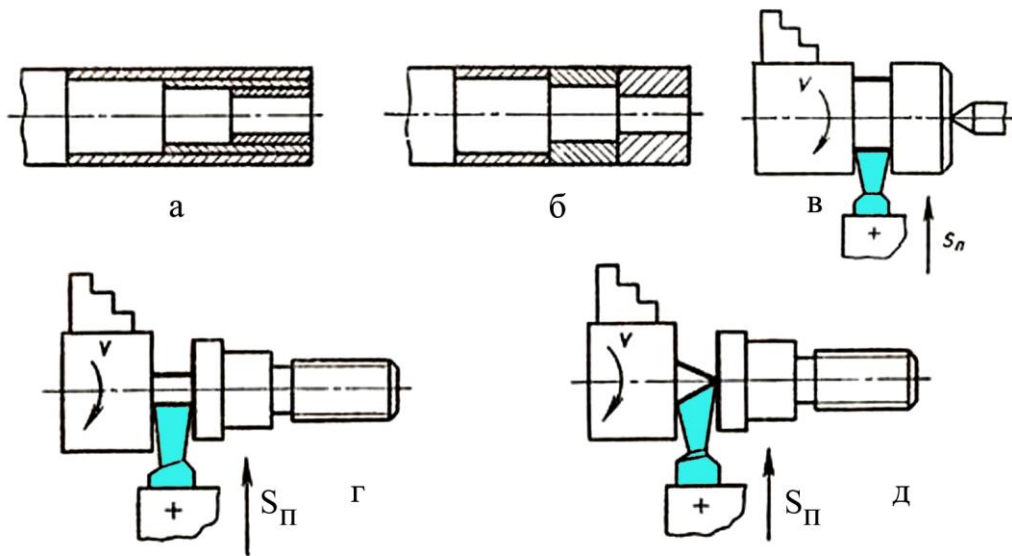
Схеми обробки заготовок на токарно-гвинторізному верстаті
